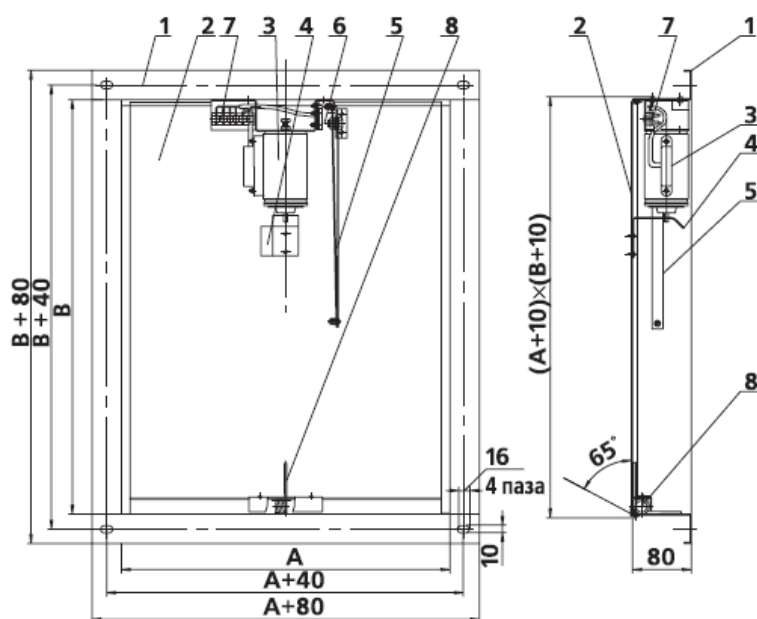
Клапан дымоудаления КПД-4-04 производства ООО «Веза» с электромагнитным приводом, установленным внутри: 1 – корпус; 2 – лопатка; 3 – электромагнит; 4 – рукоятка; 5 – ограничитель хода лопатки; 6 – конечный выключатель типа «геркон»; 7 – клеммная колодка; 8 – пружина сжатия
